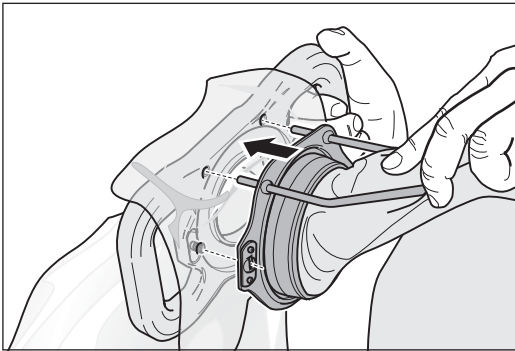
Den Staubsack mit dem Halteblech in die Entleervorrichtung einführen.
